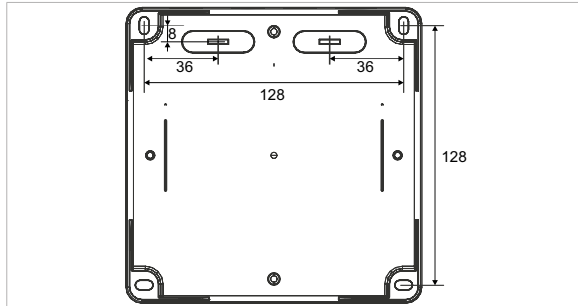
Abmessungen für Montagelöcher (Angaben in mm)
